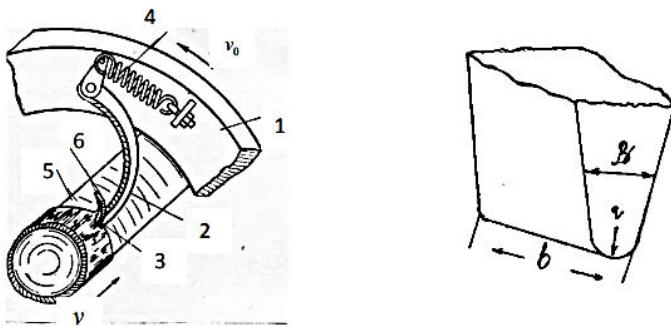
Схема работы короснимающего механизма роторного окорочного станка:
